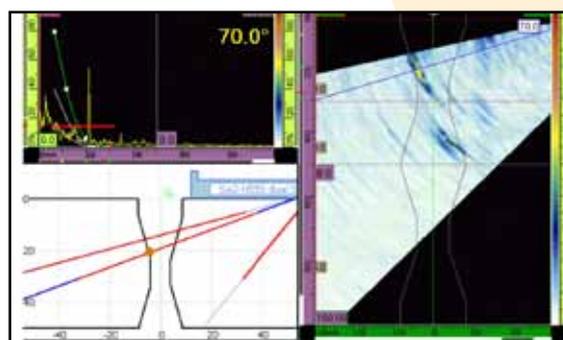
Barrido Sectorial superpuesto sobre el layout de la soldadura y vista del esquema de la soldadura con indicación de la posición del defecto. OmniScan MX manual con opción software para inspección de soldaduras
